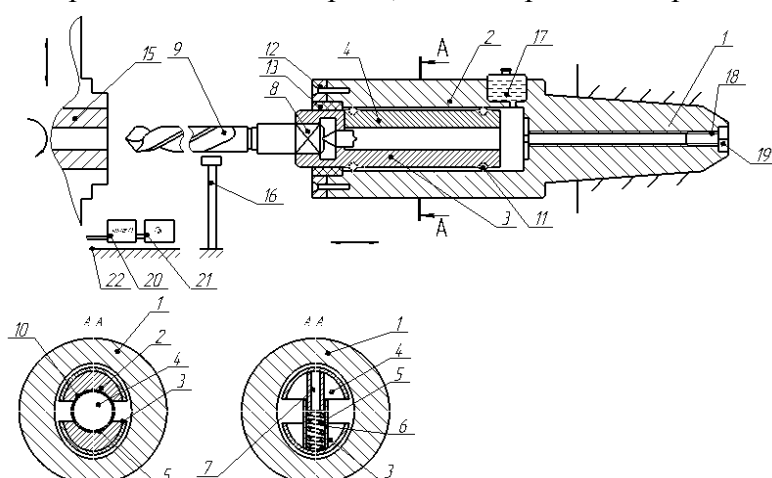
Конструкція патрона для обробки деталей пальцевим ріжучим інструментом
